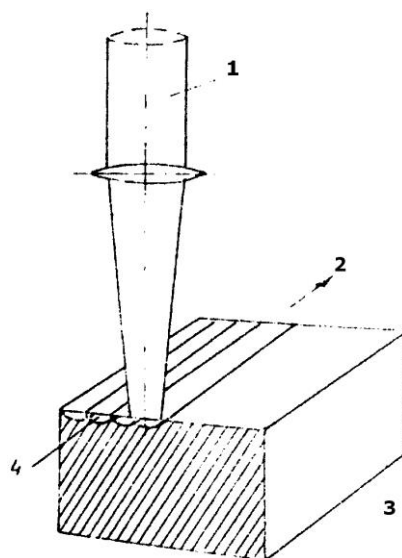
Схема процесса лазерной обработки поверхности: 1 - лазерный луч; 2 - направление движения изделия; 3 - обрабатываемое изделие; 4 - зона обработки поверхности.
